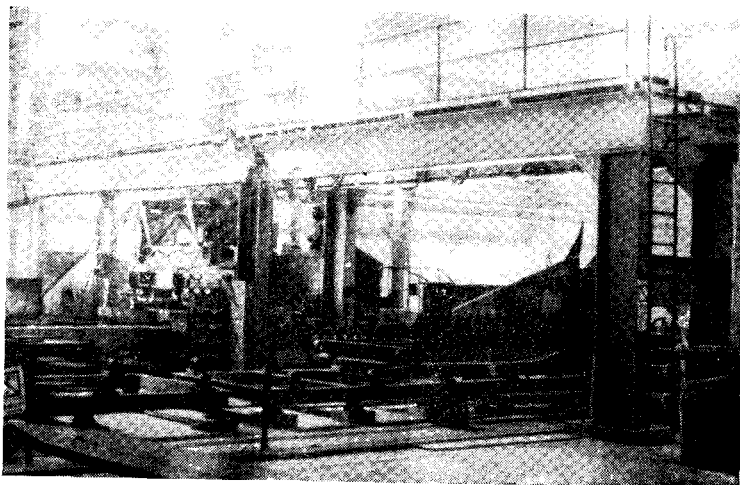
Автоматическая машина для узловой сборки корпусных конструкций.
